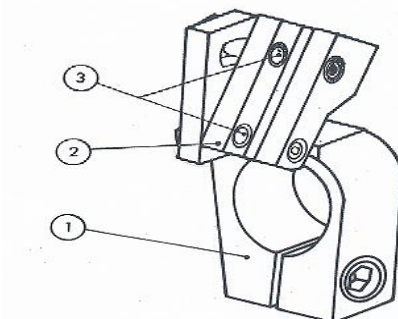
Dessin du porte-outil sur broches de perçage.
